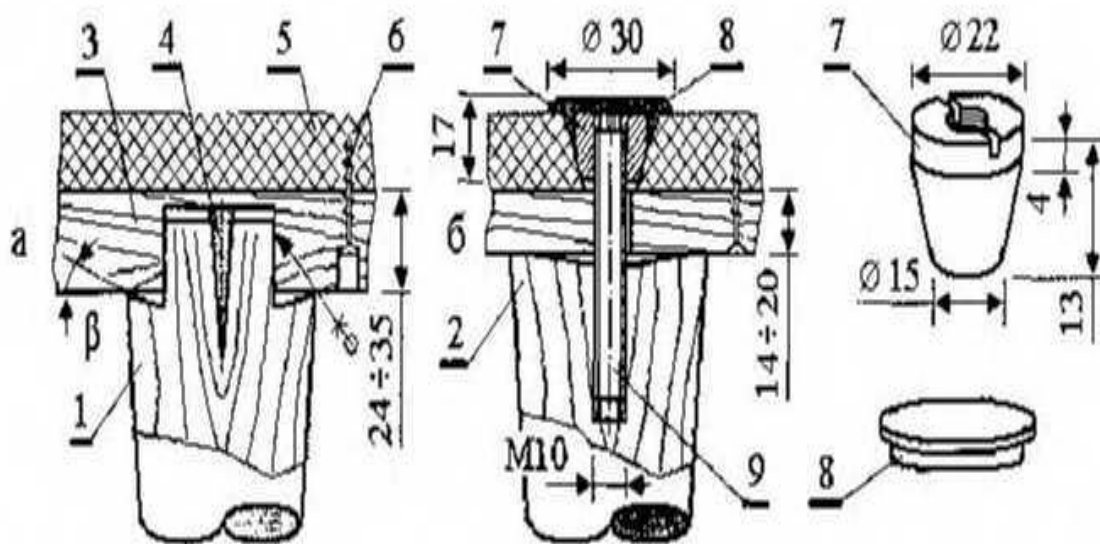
Ніжки підсадні, кріплення: а - на клею, б - на шпильці і конічній гайці; 1 - ніжка з точеним шипом, 2 - ніжка з шпилькою, 3 - брусок жорсткості, 4 - клин, 5 - долішня стінка корпусу, 6 - шуруп, 7— гайка конічна, 8 - заслінка, 9 - шпилька
